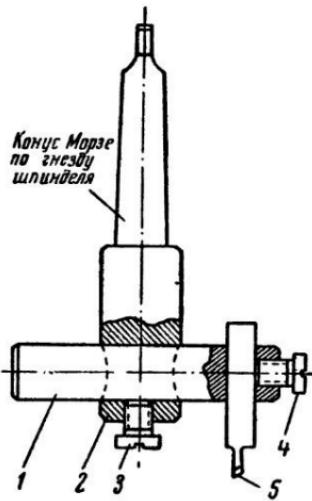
Приспособление для вырезания и растачивания на сверлильных и фрезерных станках: 1 — стержень-державка для резца; 2 — стержень-корпус; 3 — винт крепления стержня-державки; 4 — винт крепления резца; 5 — резец.
